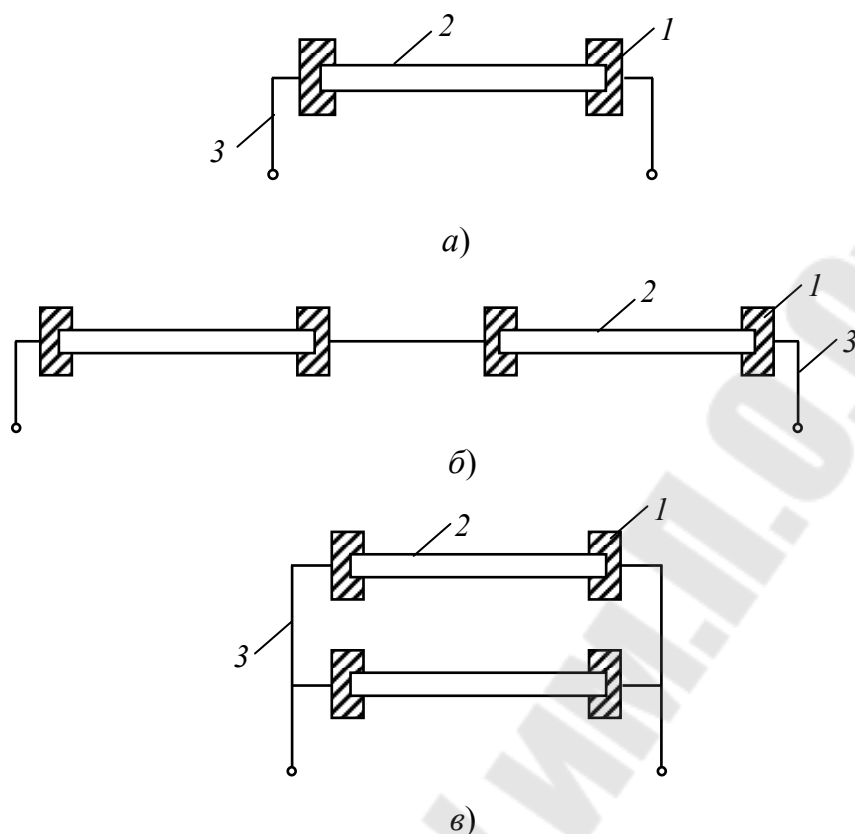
Схемы однопозиционного (а) и многопозиционных устройств с последовательным (б) и параллельным (в) включением заготовок в электрическую цепь: 1 – зажимной токоподводящий контакт; 2 – нагреваемая заготовка; 3 – токопроводящий провод
